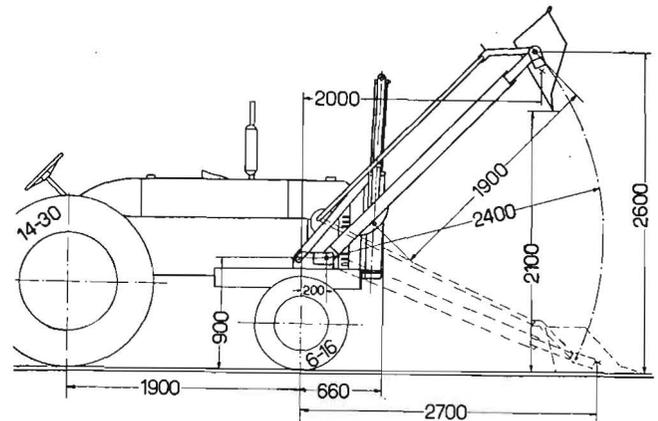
McCormick WD 6 mit Jayhawk-Lader. Hubweg der Schaufel 2490 mm; Hubweg des Kolbens 560 mm; Durchmesser des Kolbens: 100 mm
